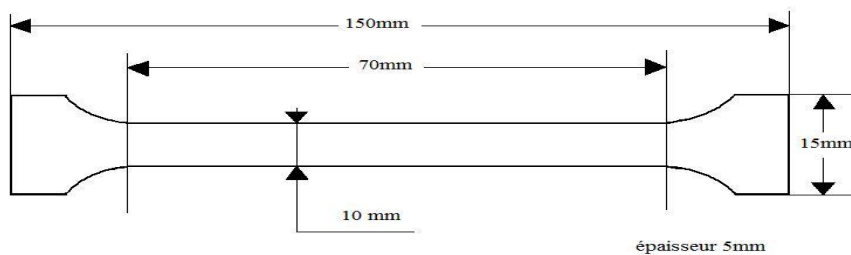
Éprouvettes en forme d'haltère de la résine
